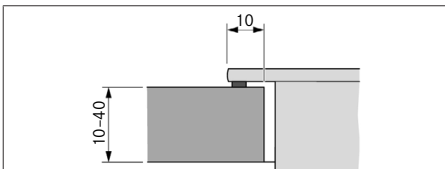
Wielkość zakładki przy montażu z zachowaniem równej powierzchni
